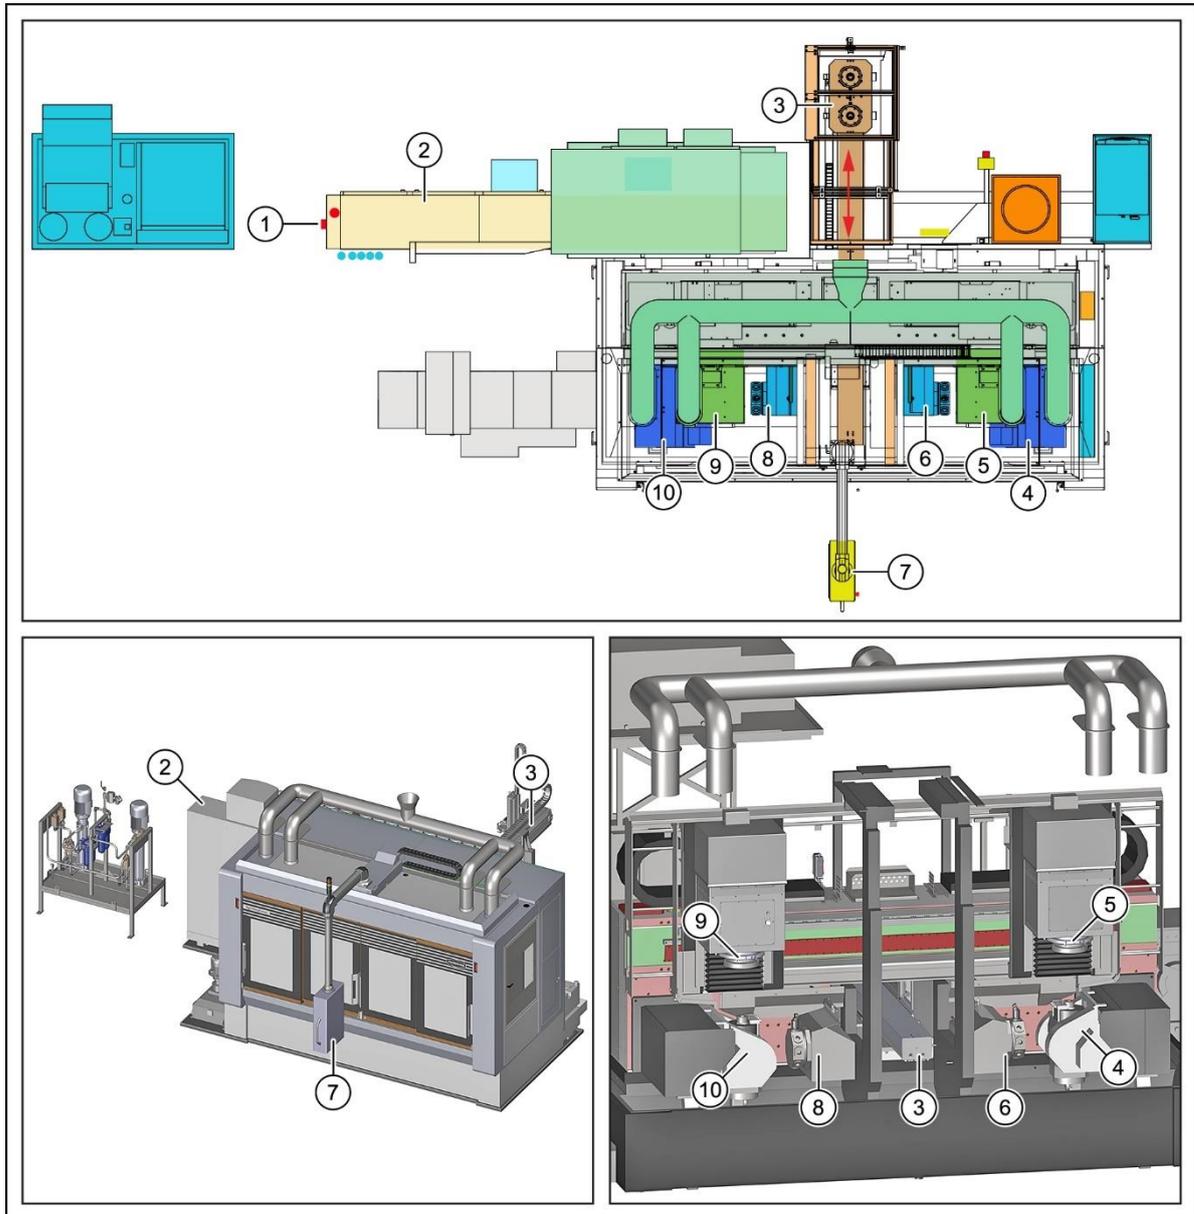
Baugruppenübersicht Innenhon-/ Wälzschälmaschine SynchroForm (Beispiel)
